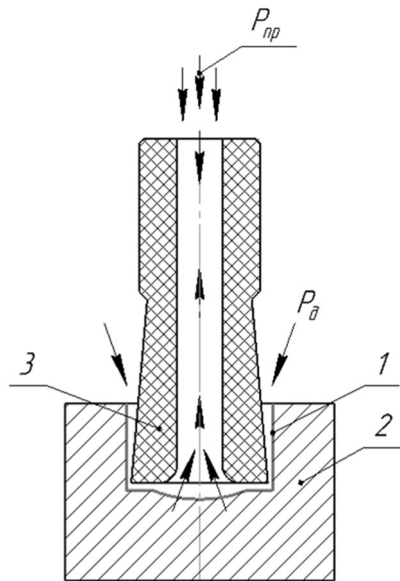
Схема формоутворення чистої обробки по внутрішньому контуру
